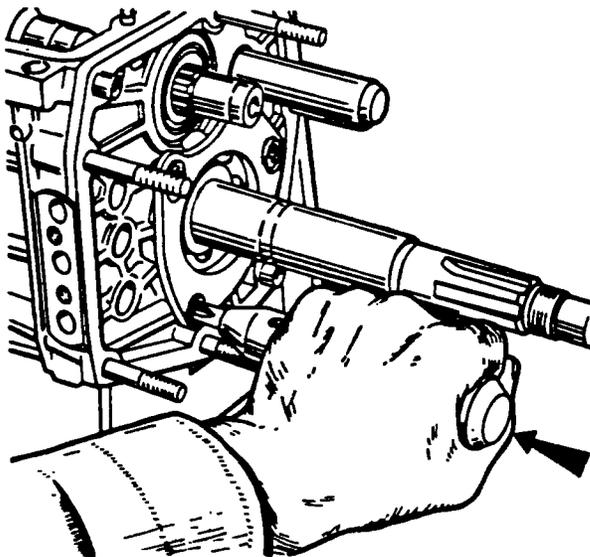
Отвртывание винтов крепления стопорной пластины промежуточного подшипника вторичного вала дрель-отверткой. Стрелкой показано направление ударного хода обоймы отвертки; пользуйтесь молотком
